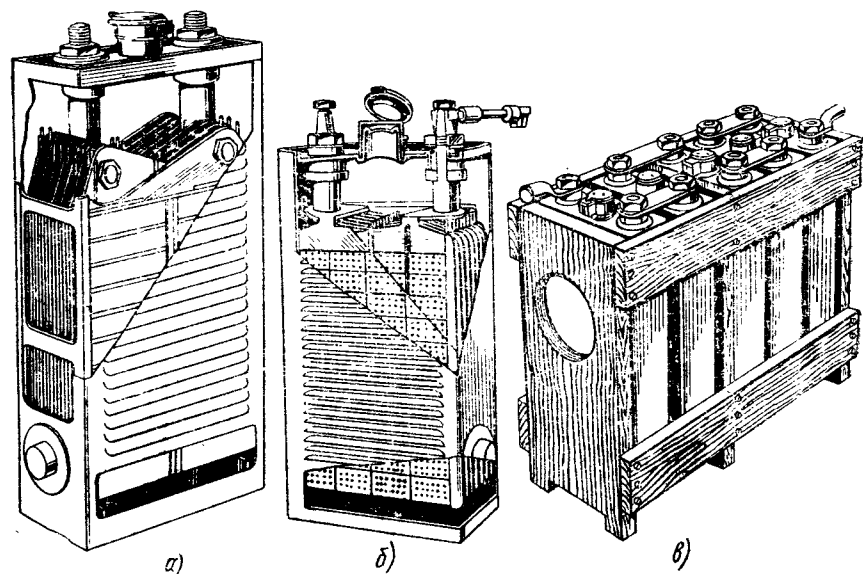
Щелочные аккумуляторы со сборкой пластин с помощью соединительных стержней (а), со сборкой с помощью сварки (б) и шестивольтовая батарея (в)
